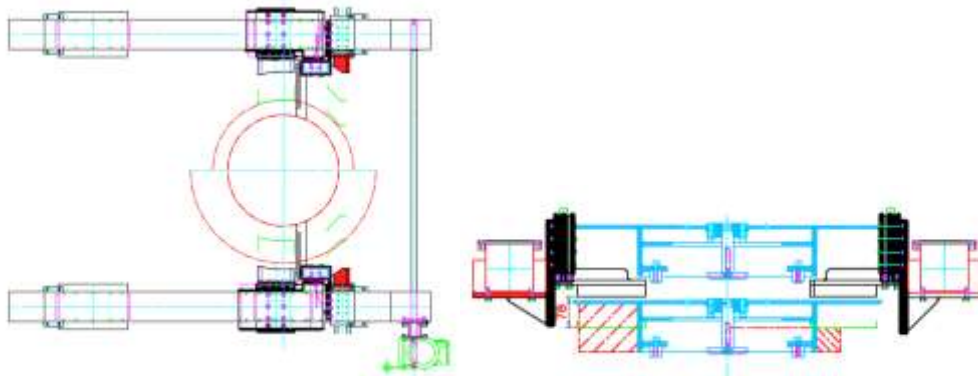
26 Vista lateral i planta del manipulador, de traslado de bobinado a flejado
